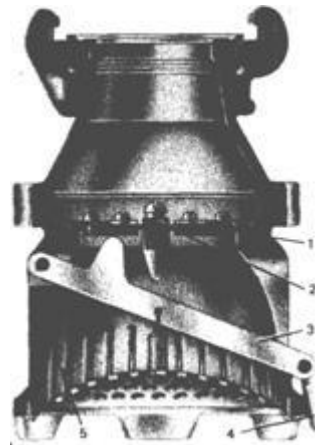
Всасывающая сетка: 1 - корпус; 2 - клапан; 3 - рычаг; 4 - кольцо; 5 - боковые прорези
